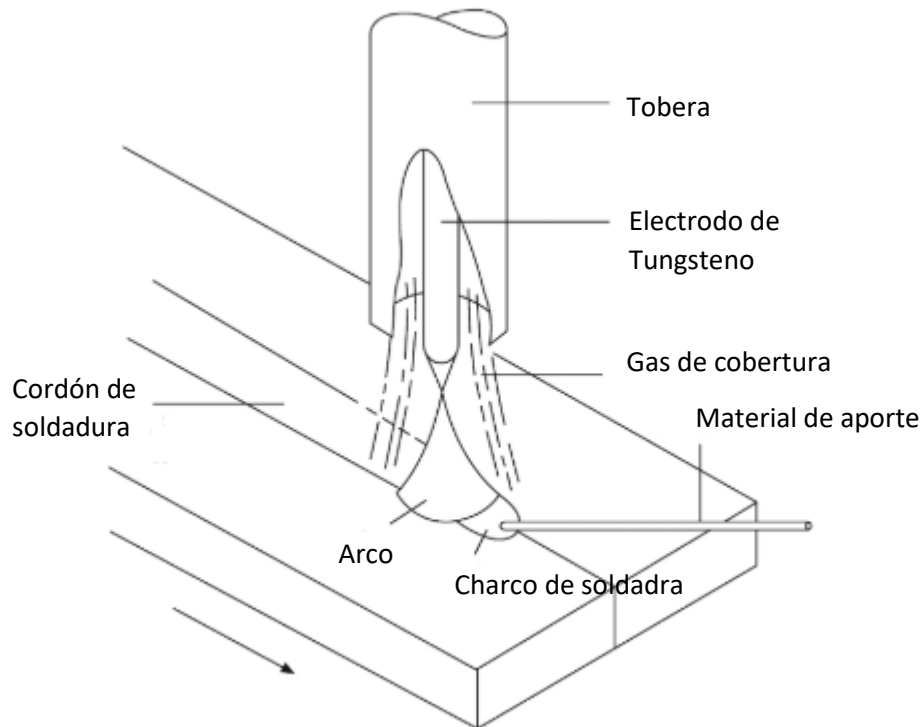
Esquema de soldadura por arco eléctrico
